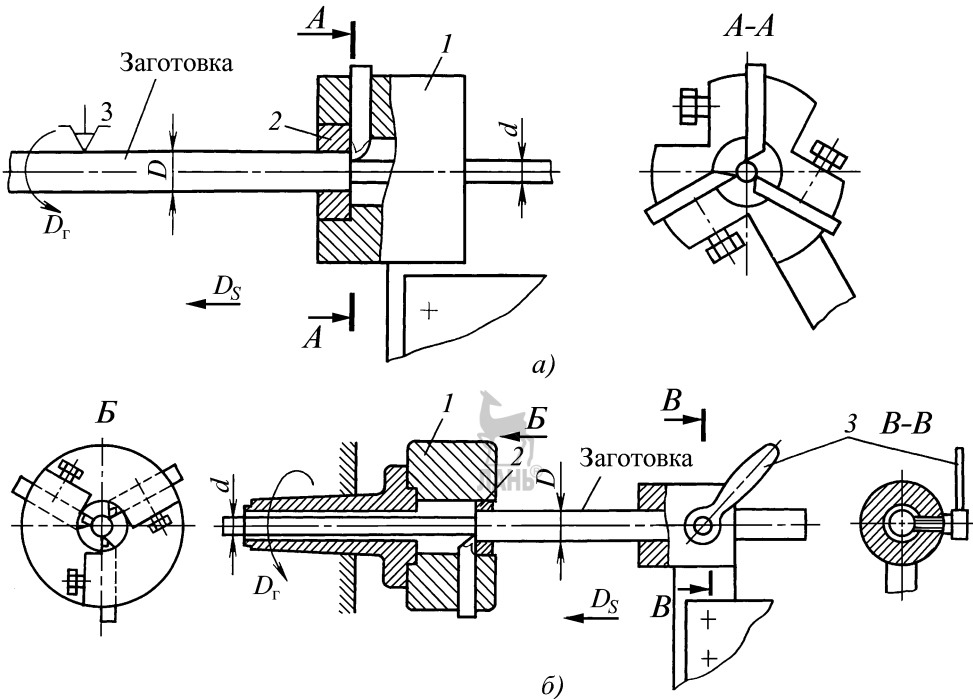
Схема обтачивания прутковой заготовки многорезцовой невращающейся (а) и вращающейся (б) головками:
